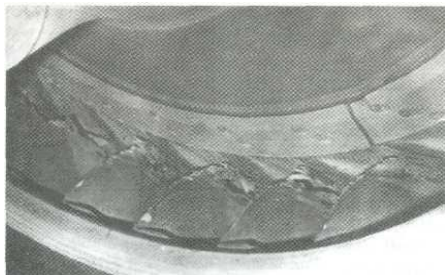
Характер ерозійного руйнування лопаток робочого колеса компресора
